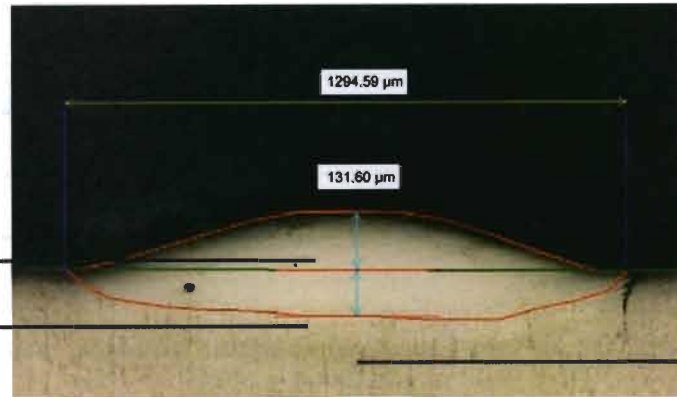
26 Cordón de soldadura #5 visto a 5X
